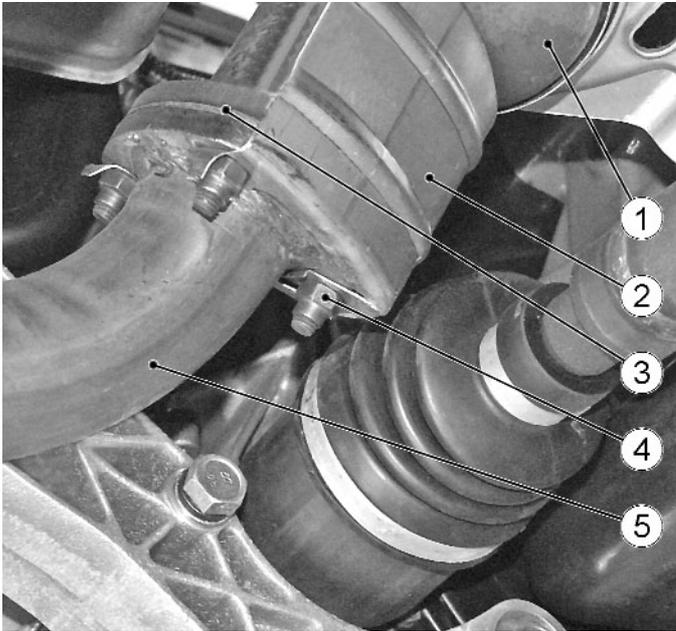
Соединение приемной трубы глушителя с нейтрализатором в сборе и дополнительного глушителя:
